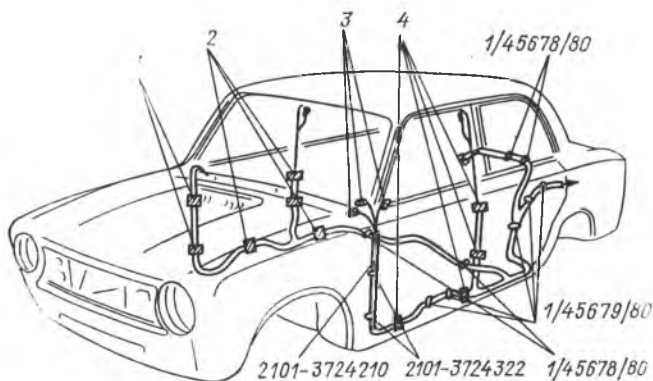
Укладка и крепление заднего пучка проводов в салоне кузова
